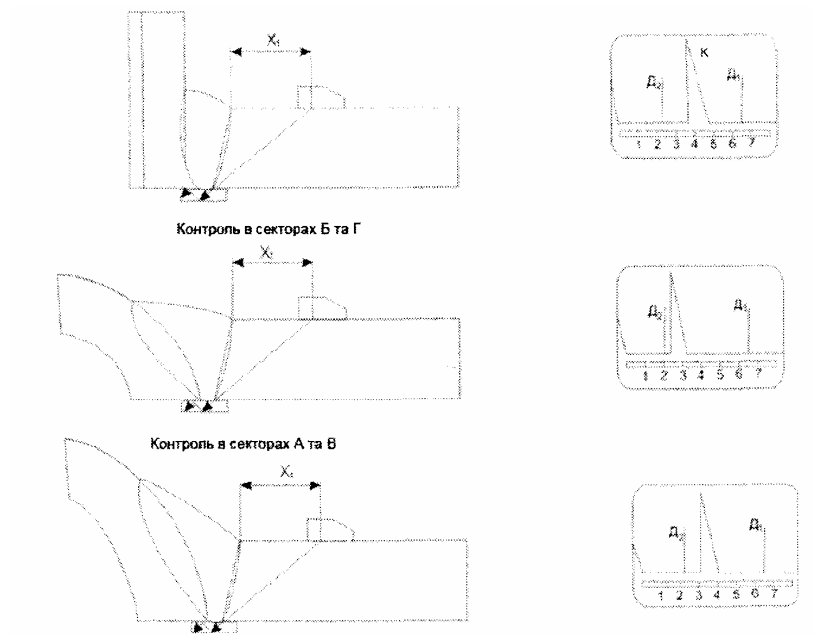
Схемы контроля углового сварного соединения в разных секторах
